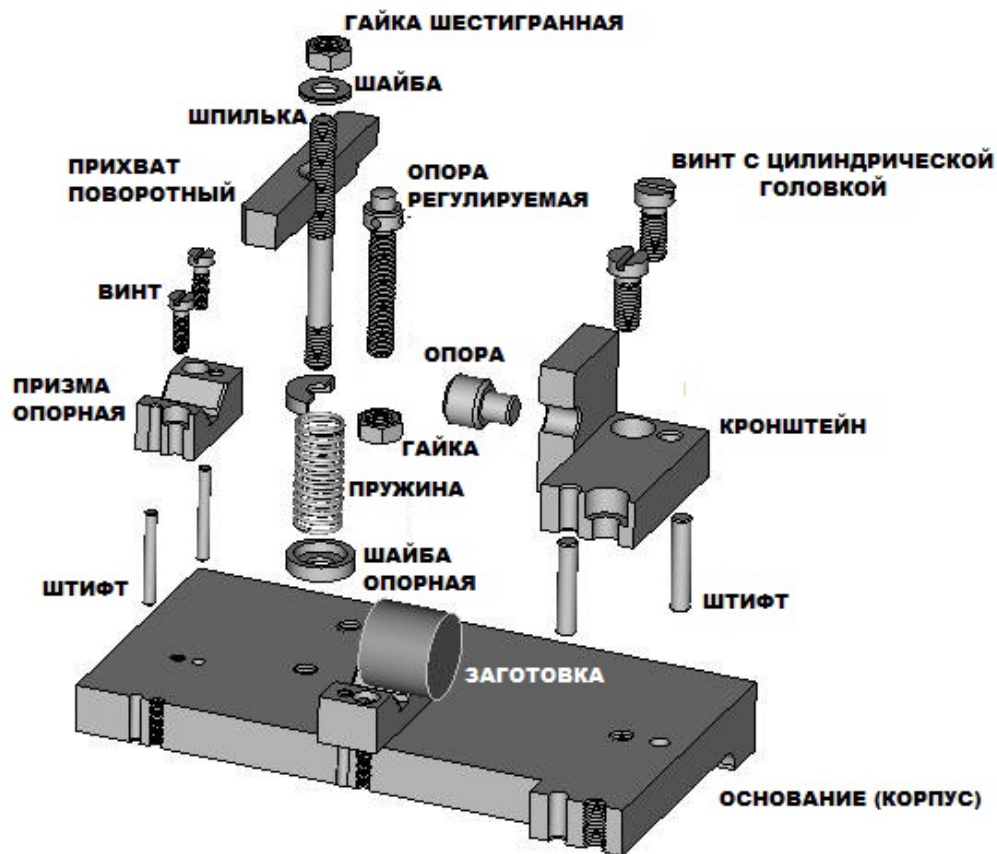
Устройство зажимного приспособления для цилиндра
